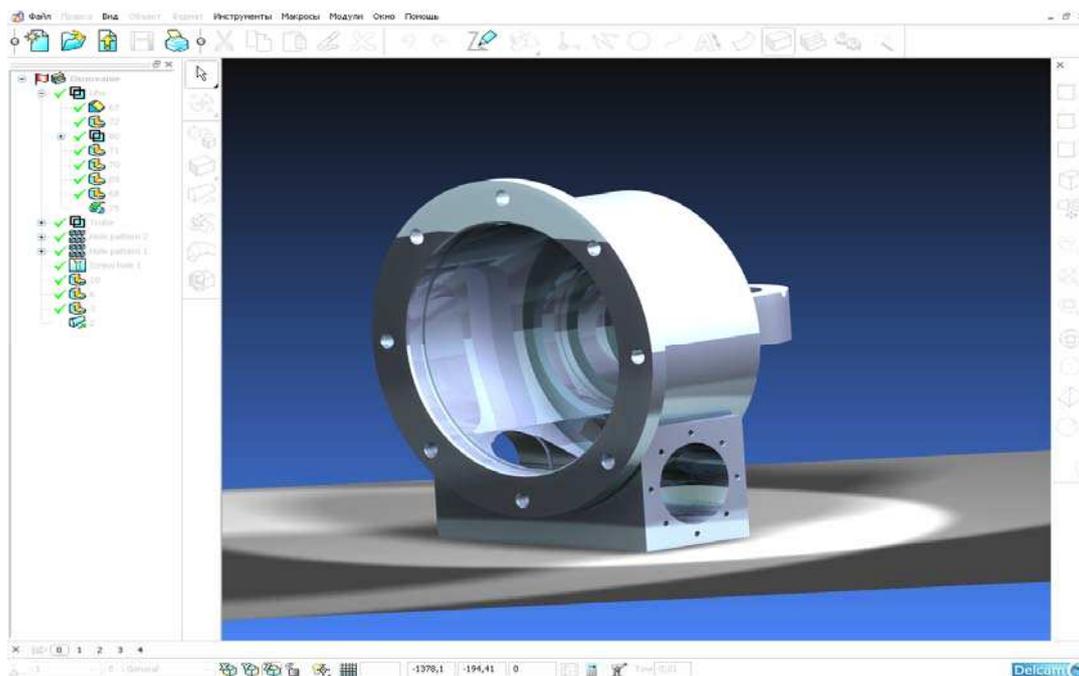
3D-модель корпуса червячного редуктора, созданная в среде Power Shape
